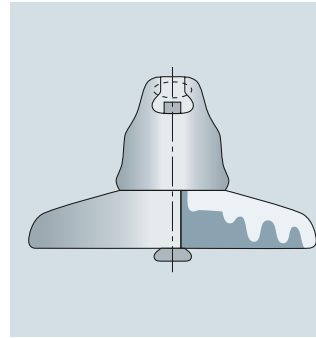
Aislador de tapa y pasador (sobre)
